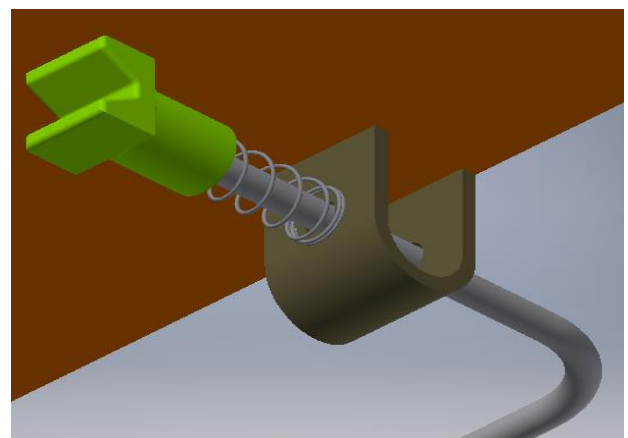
Prismă mobilă (detaliu sistem de prindere cu prisme mobile)
